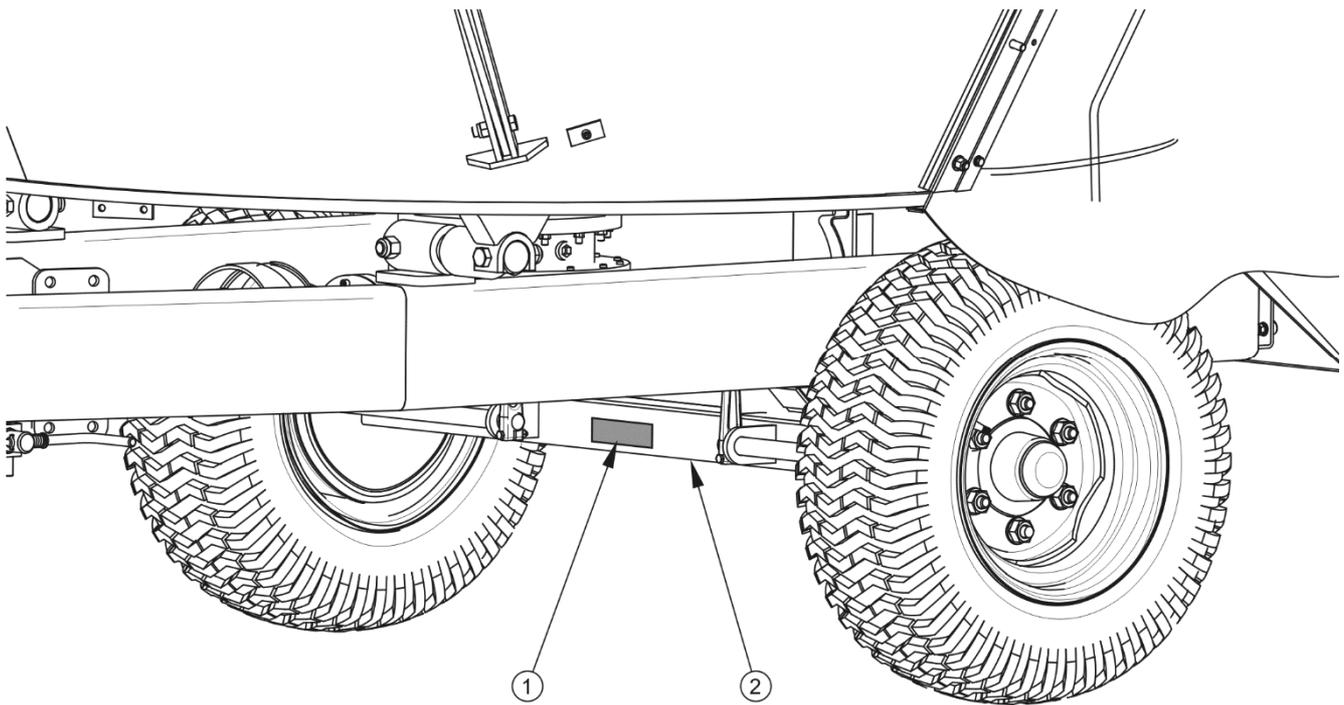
Emplacement de la plaque signalétique de l’essieu moteur
